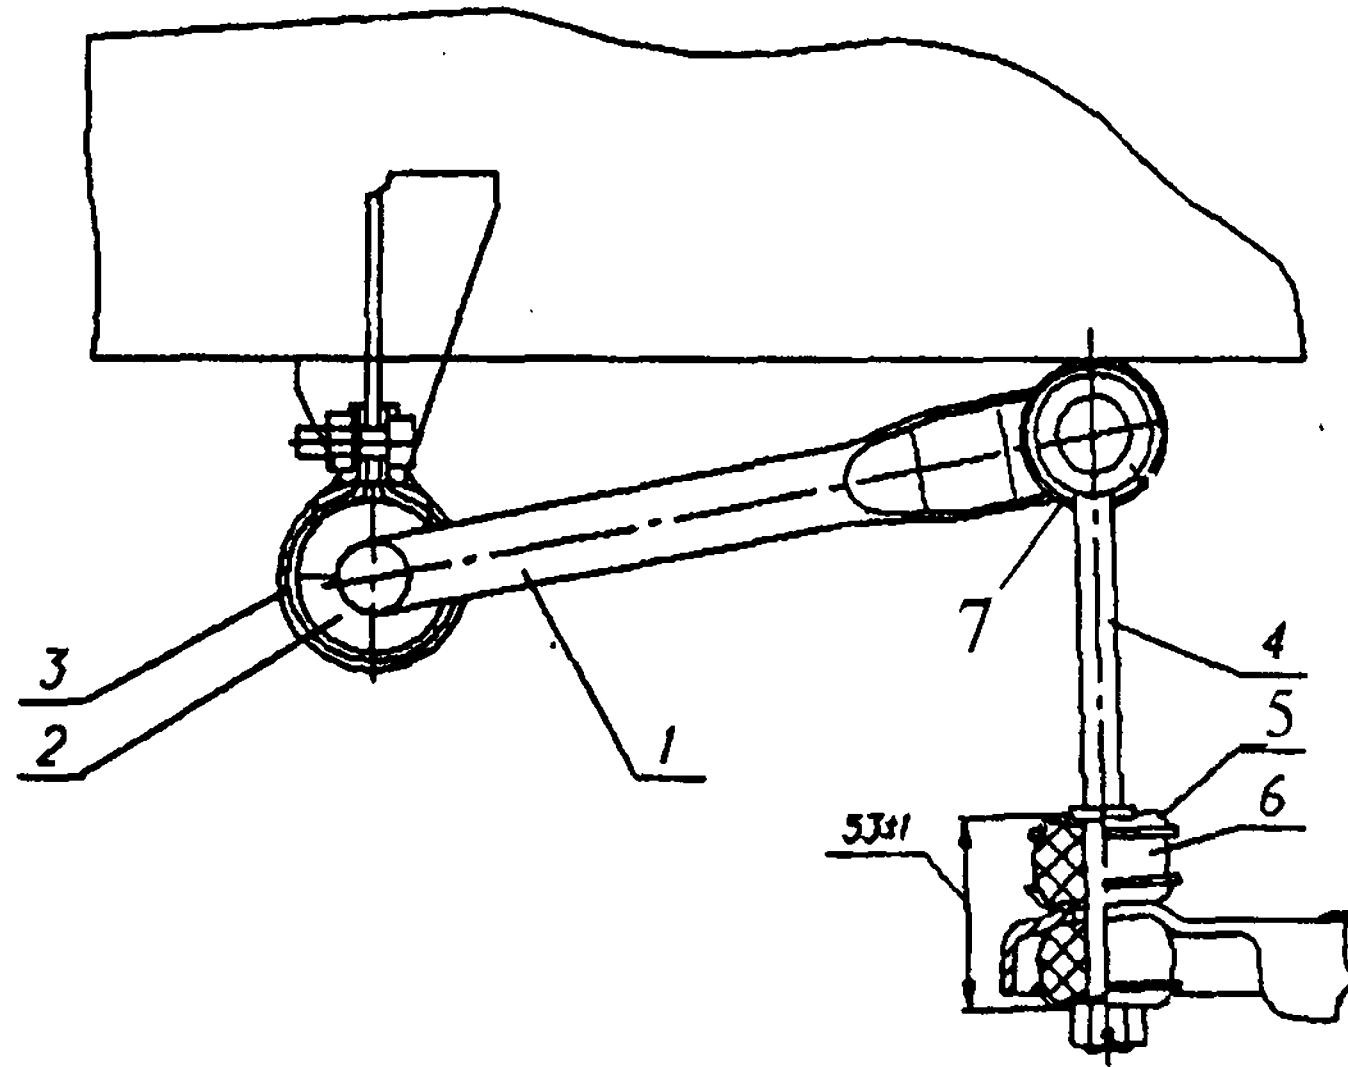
Стабилизатор передней подвески: 1 – штанга стабилизатора; 2 – обойма; 3 – втулки; 4 – стойка стабилизатора с шаровым шарниром в сборе; 5 – чашка; 6 – подушка резиновая; 7 – шарнир неразборный
